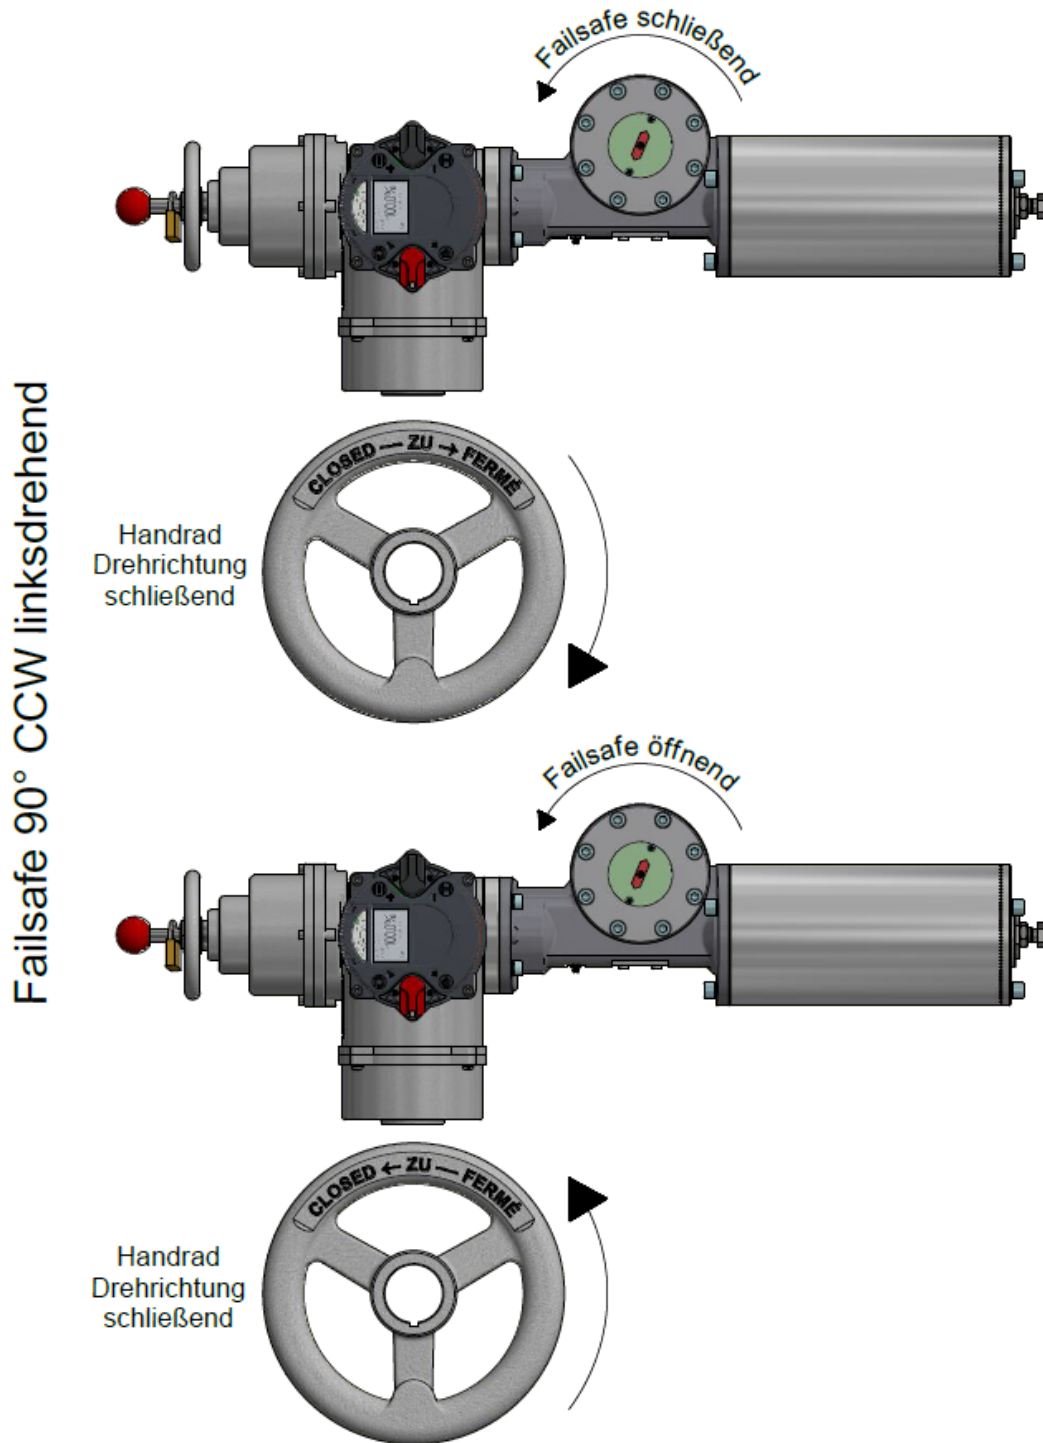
Drehrichtung des Handrades für Failsafe „CCW“.
